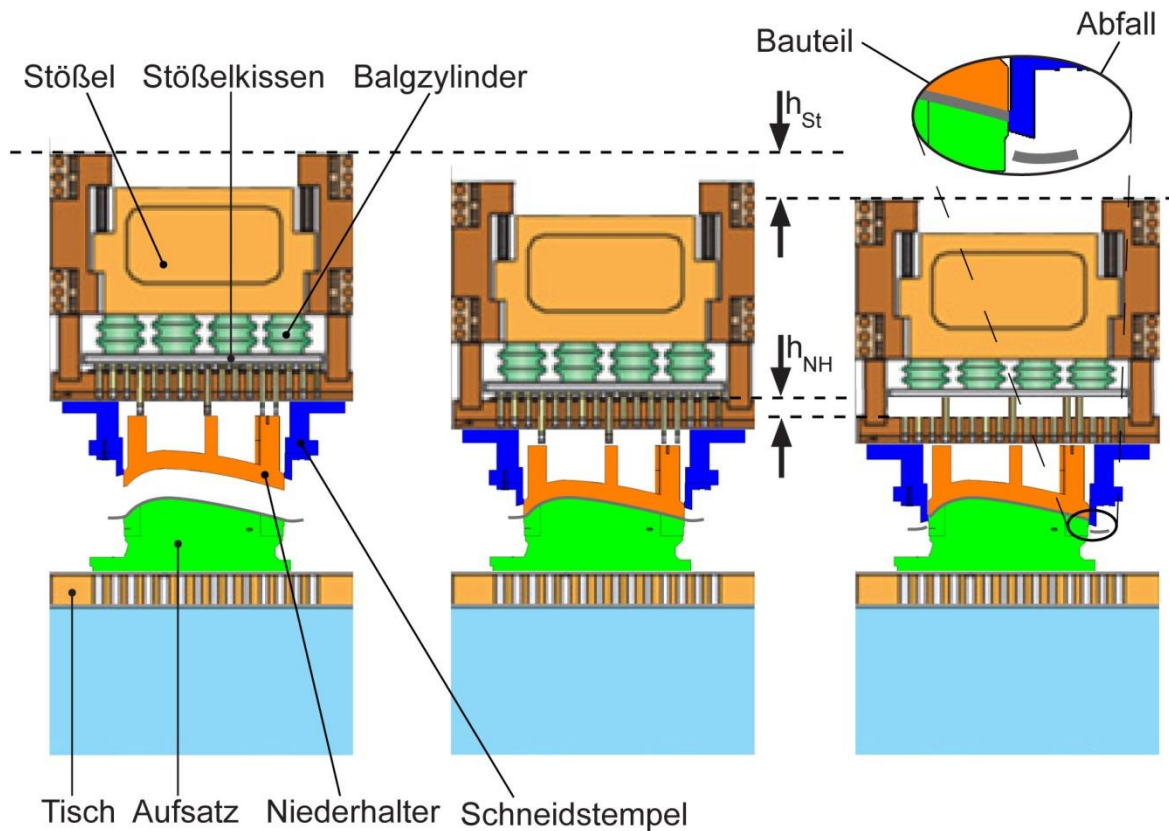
Funktionsprinzip Beschneidewerkzeug: links geöffnetes Werkzeug, Mitte Niederhalter schließen, rechts Werkzeug in UU
